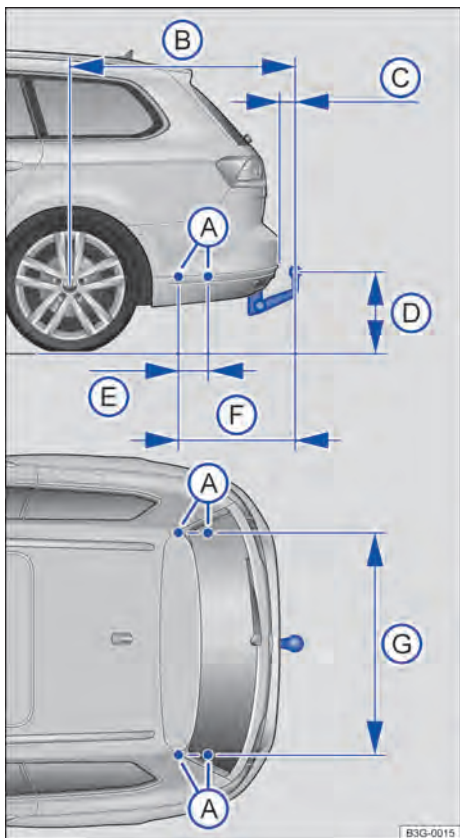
Dimensões e pontos de fixação para instalação posterior de um dispositivo de reboque (Passat Variant).
